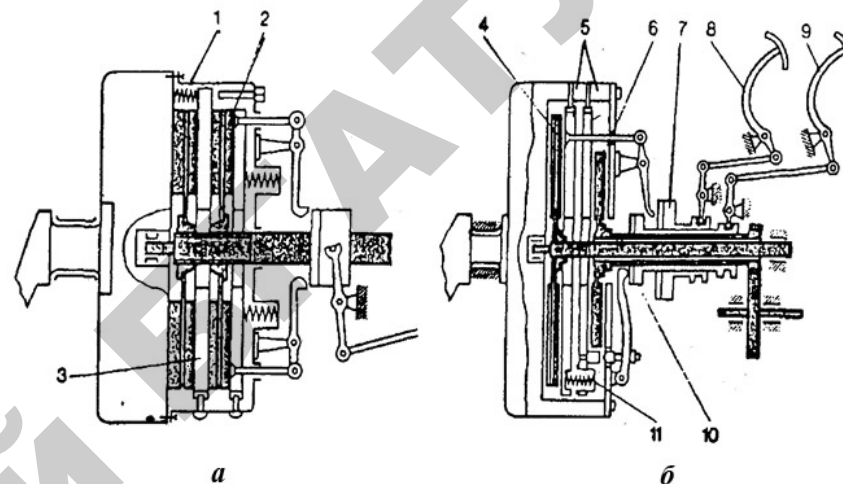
Схемы однопоточного и двухпоточного сцеплений
